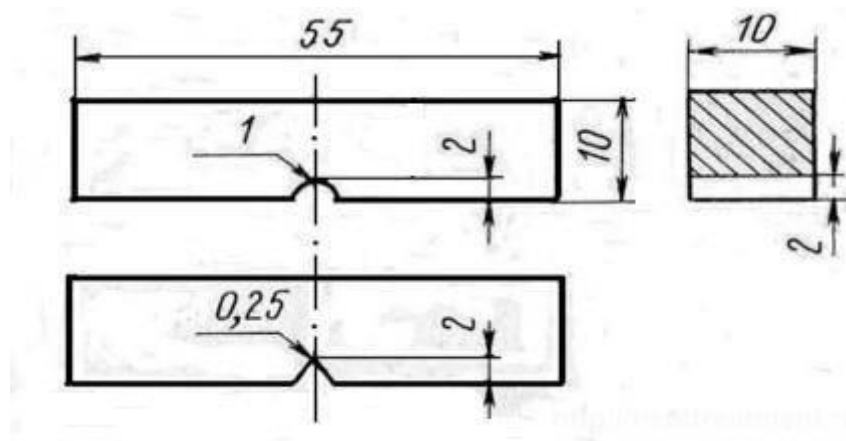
стандартные образцы для испытания на ударную вязкость
